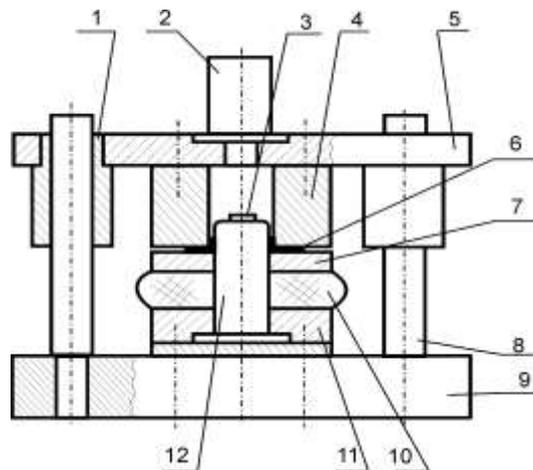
Конструкція штампа для відбуртовування отворів: 1 – направляюча втулка; 2 – хвостовик; 3 – фіксатор; 4 – матриця; 5 – плита верхня; 6 – заготовка; 7 – кільце притискне; 8 – колонка; 9 – плита нижня; 10 – гумовий демпфер; 11 – пуансонотримач; 12 – пуансон
